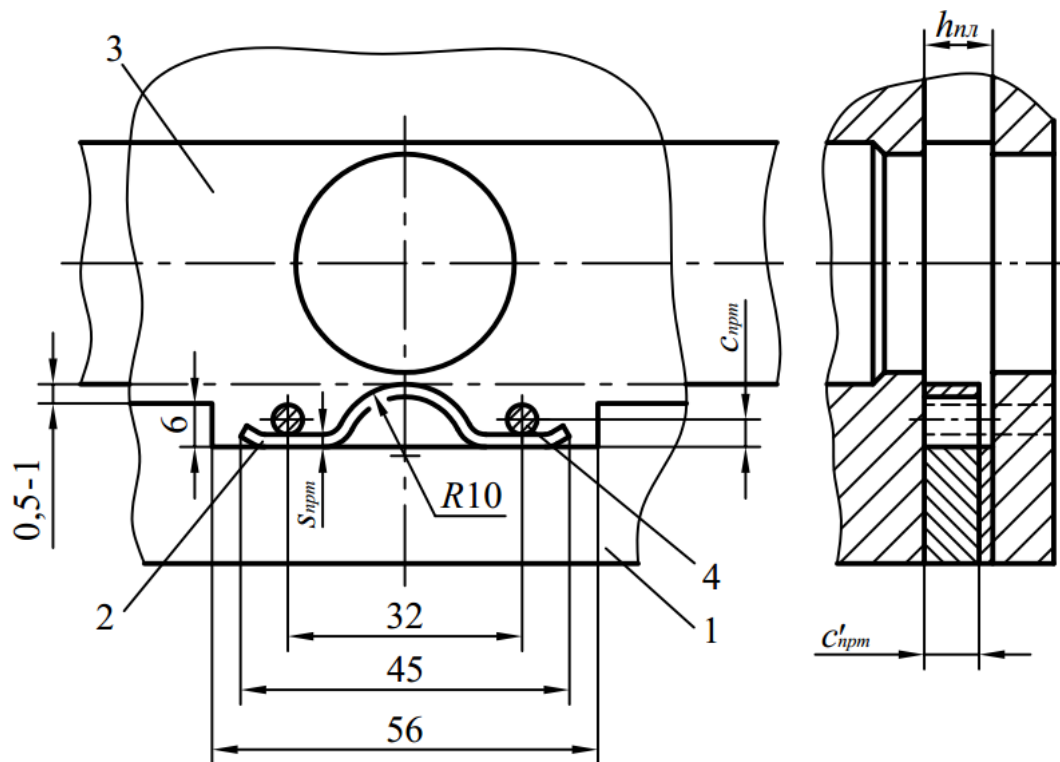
Конструкція напрямної планки з пружинним притискувачем смуги:
